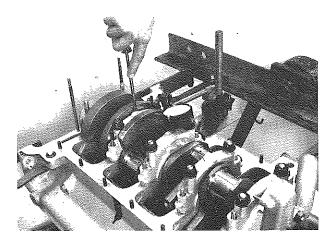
Verificare il gioco assiale Checking axial clearance
